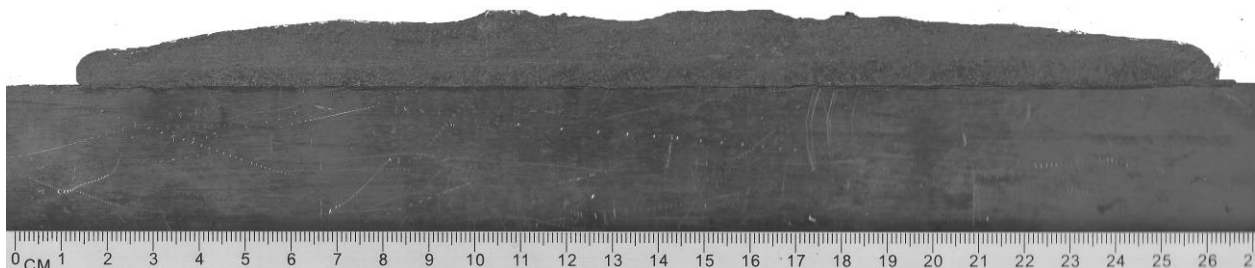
Образец, наплавленный многоэлектродной наплавкой
